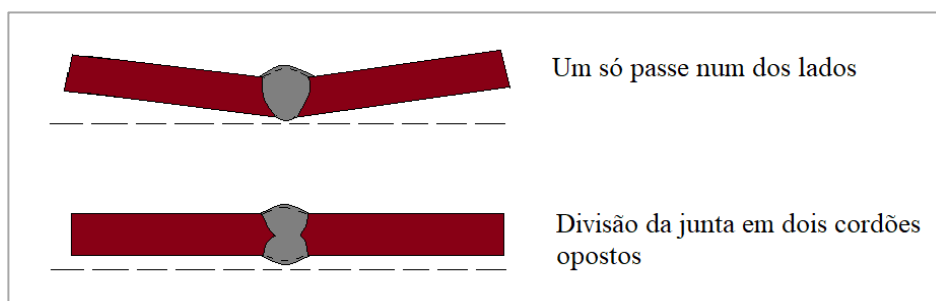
Divisão da junta em dois cordões de soldadura opostos – [10] imagem adaptada
